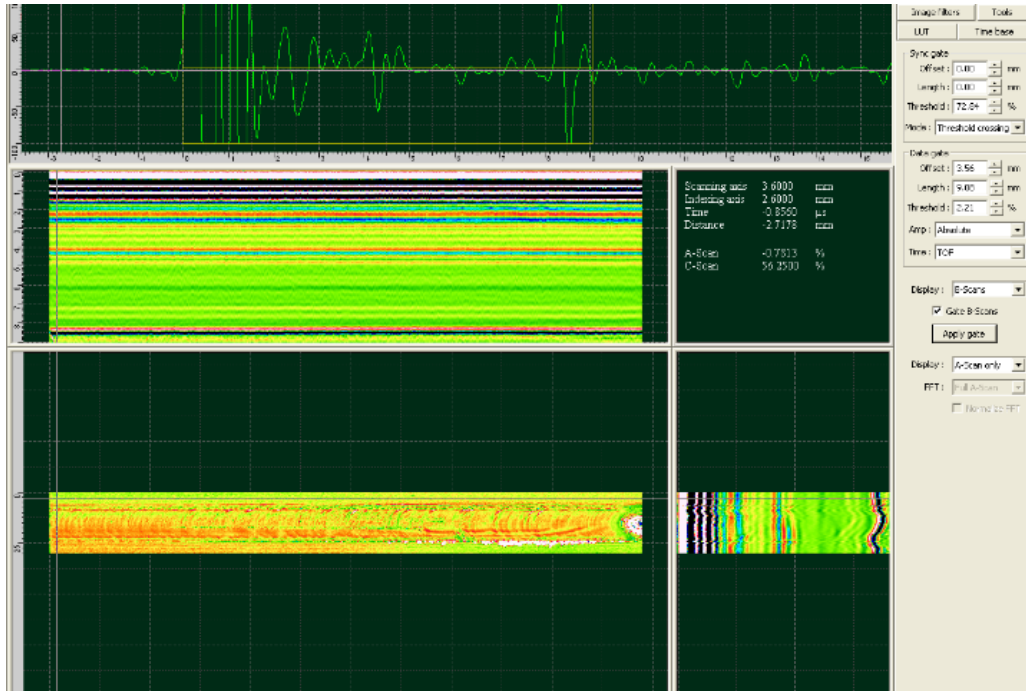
Test finaux 300 mm d'extrusion soudés (fin de la zone soudée)
